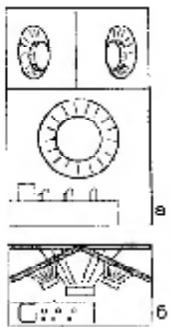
Конструкция контрольного агрегата: а — вид спереди; б — вид сбоку
